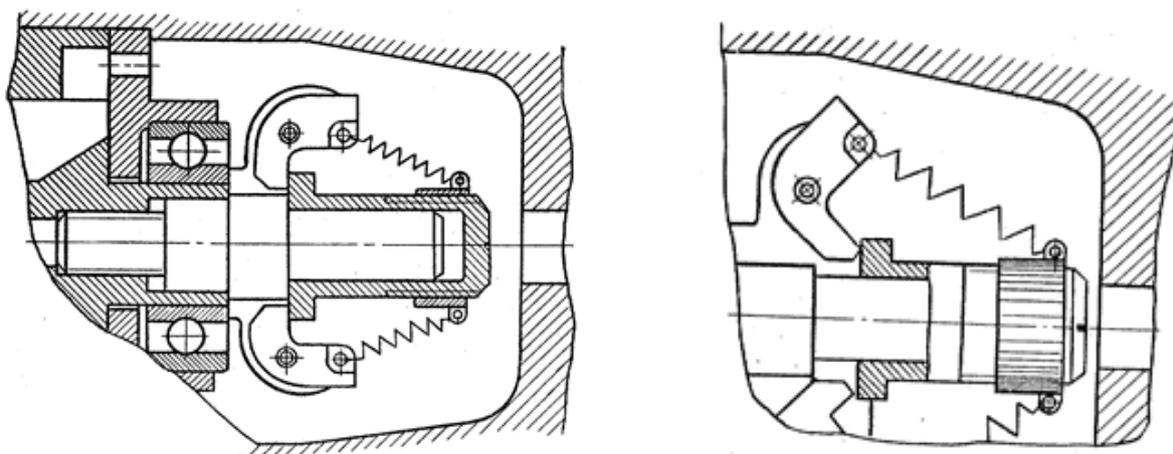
Центробежный регулятор оборотов пневматических ручных машин [9]
